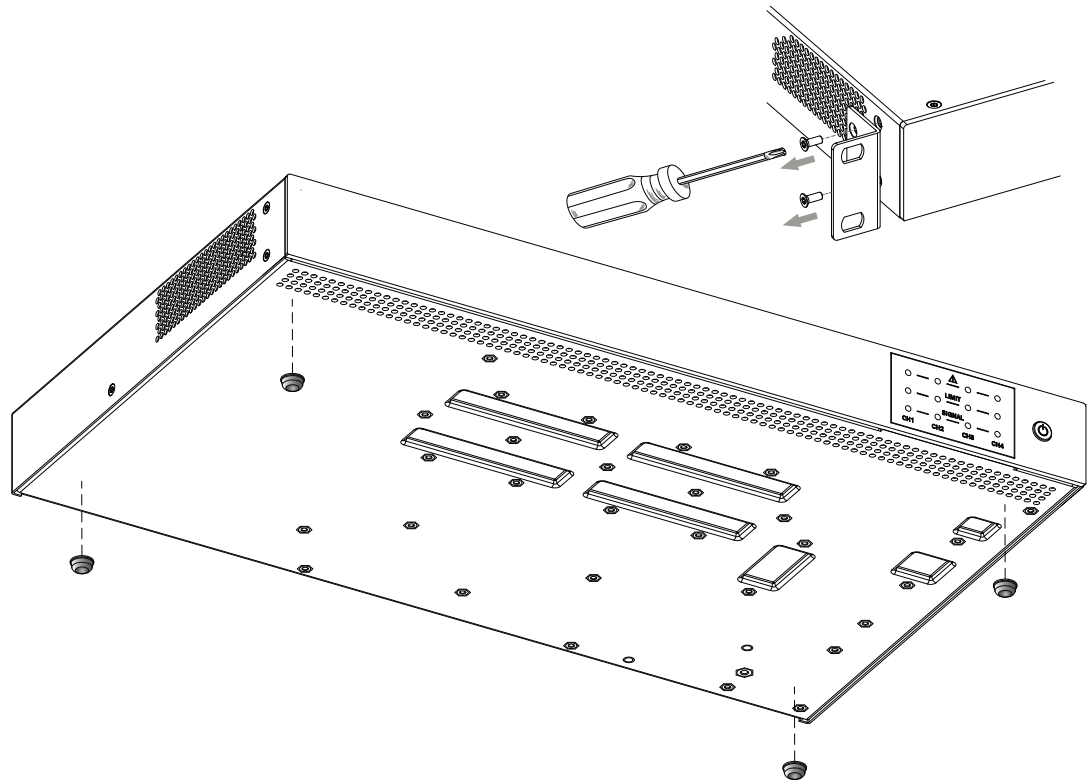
Demontage der Rackmontagewinkel (oben rechts) und Anbringen der GummifüÙe (unten)
